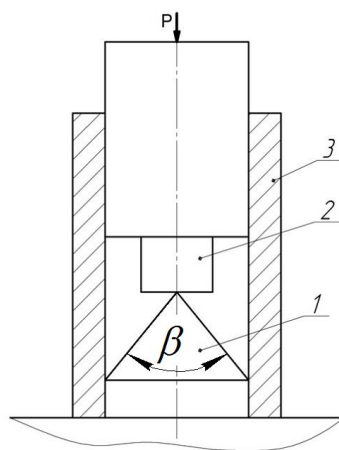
Пристрій для визначення ступеня зміцнення досліджуваних матеріалів: 1 - конічний зразок; 2 - твердосплавний бойок; 3 - напрямна втулка
